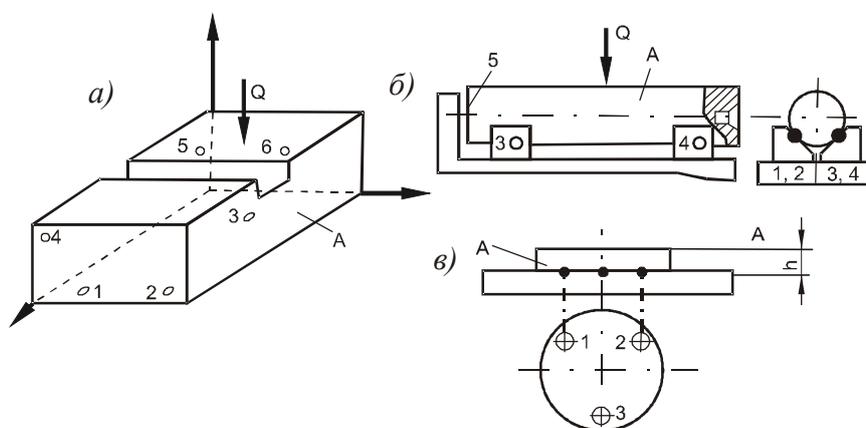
Схема установки заготовок с лишением различного количества степеней свободы:
